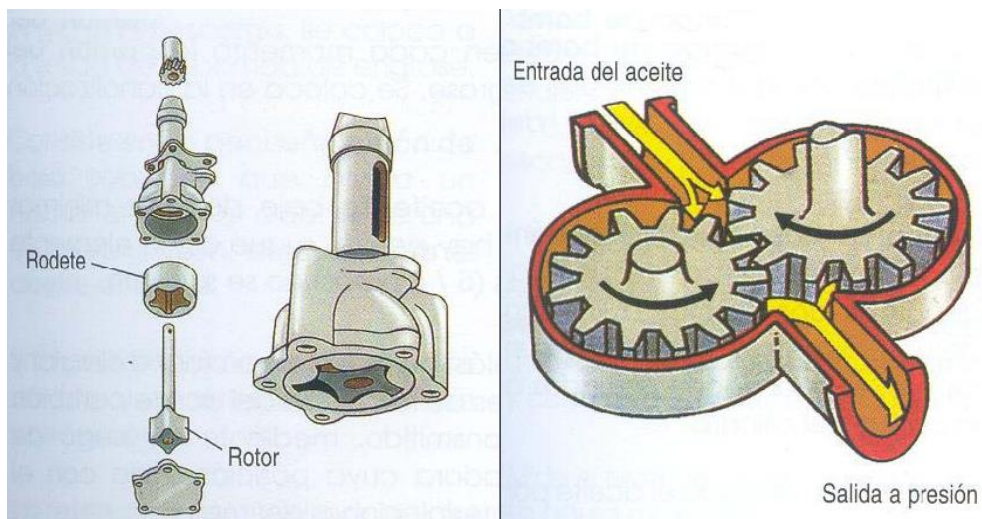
Bomba de lóbulos y bomba de engranajes. ⁴⁶
